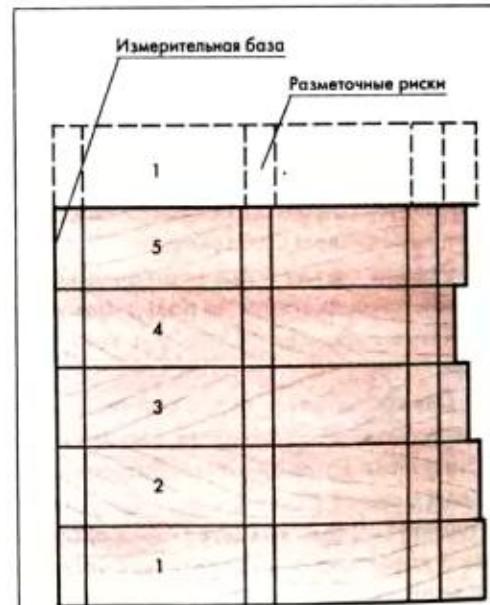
Схема сравнительного контроля точности разметки заготовок
